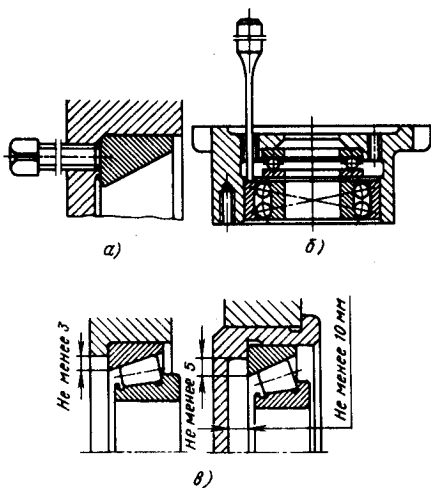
Конструктивные элементы подшипниковых узлов, облегчающие их демонтаж
